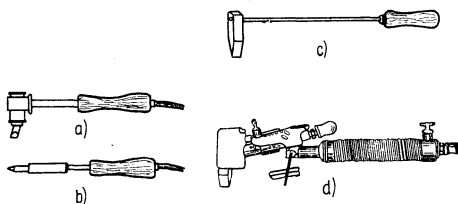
Lötwerkzeuge; elektrischer LötKolben größerer Leistung (a), normaler RadiolötKolben (b), HammerlötKolben (c) und BenzinlötKolben (d)
